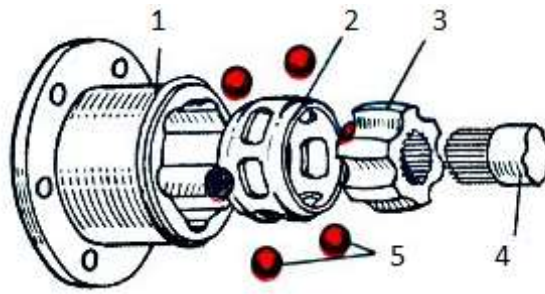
Кульковий шарнір з ділительними канавками, що допускає осьове переміщення валів: 1 – корпус; 2 – сепаратор;
